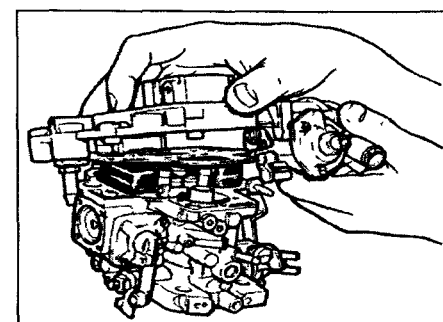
Снятие верхнего корпуса (крышки) карбюратора
